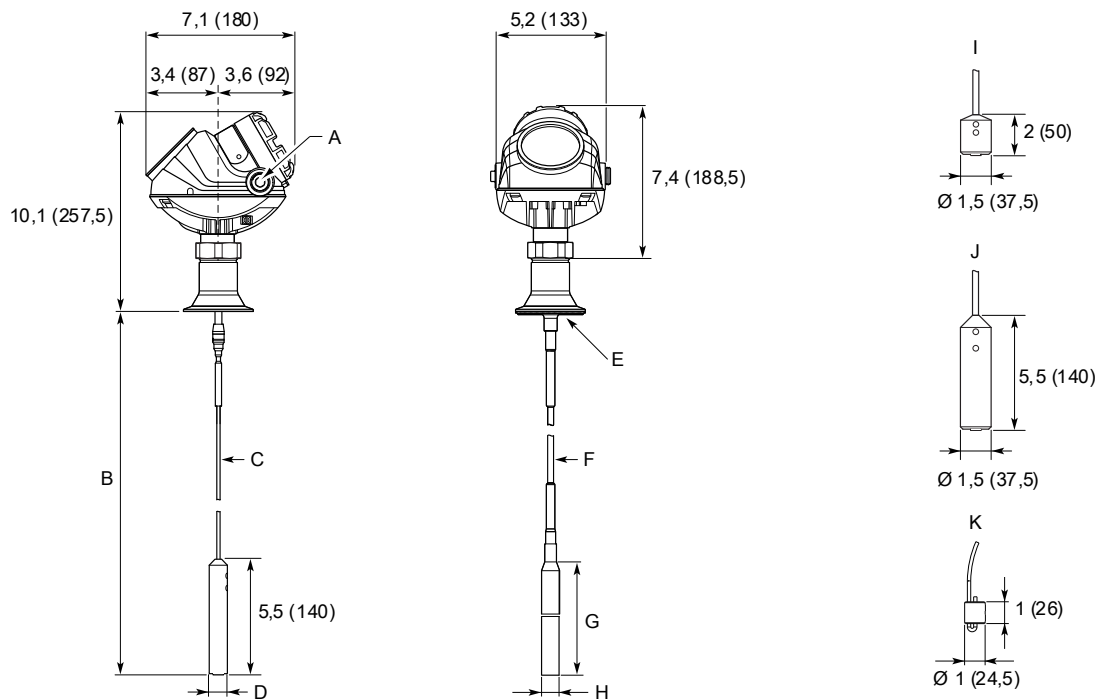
Antena de condutor flexível simples com conexão de flange
